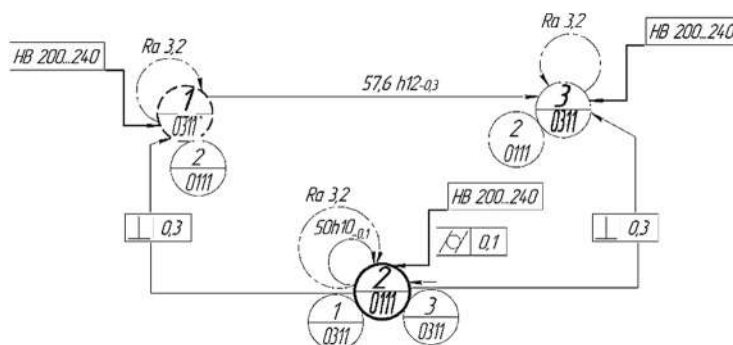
Граф размерных связей между элементарными поверхностями заготовки детали «Валик» (прокат)
